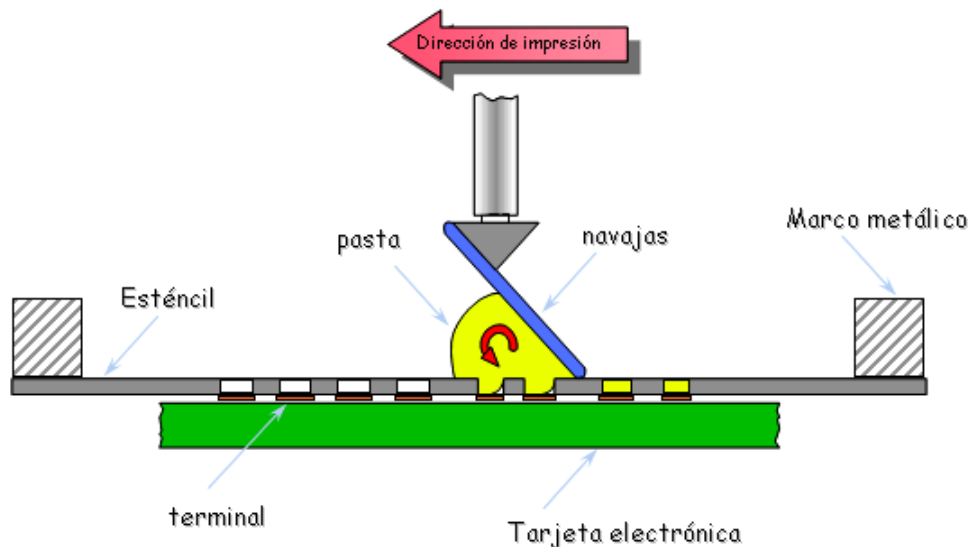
Proceso de impresión de soldadura.
